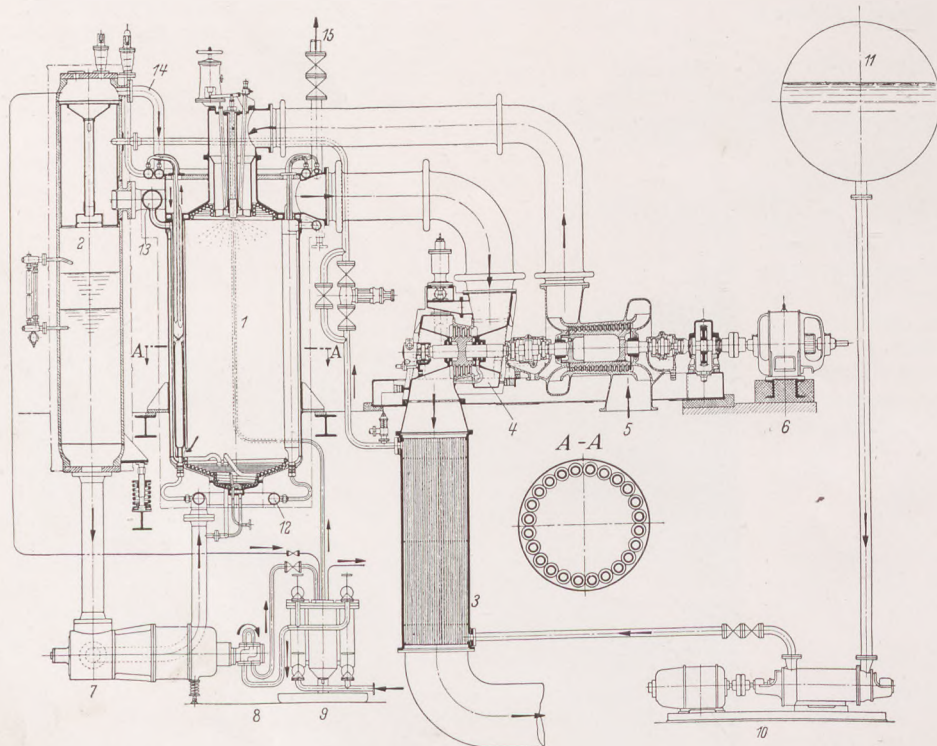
Schnitt durch einen ölgefeuerten Velox-Dampferzeuger mit eingebautem Überhitzer und elektrisch angetriebenen Hilfsmaschinen.
